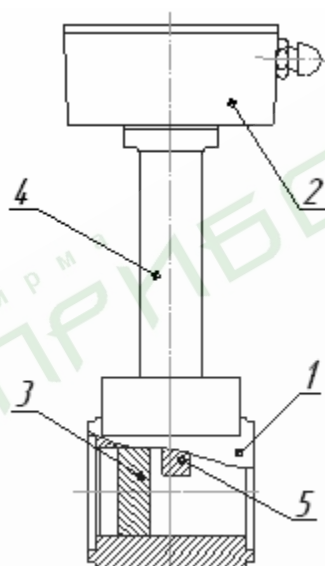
Устройство преобразователя расхода , 1 - корпус;
